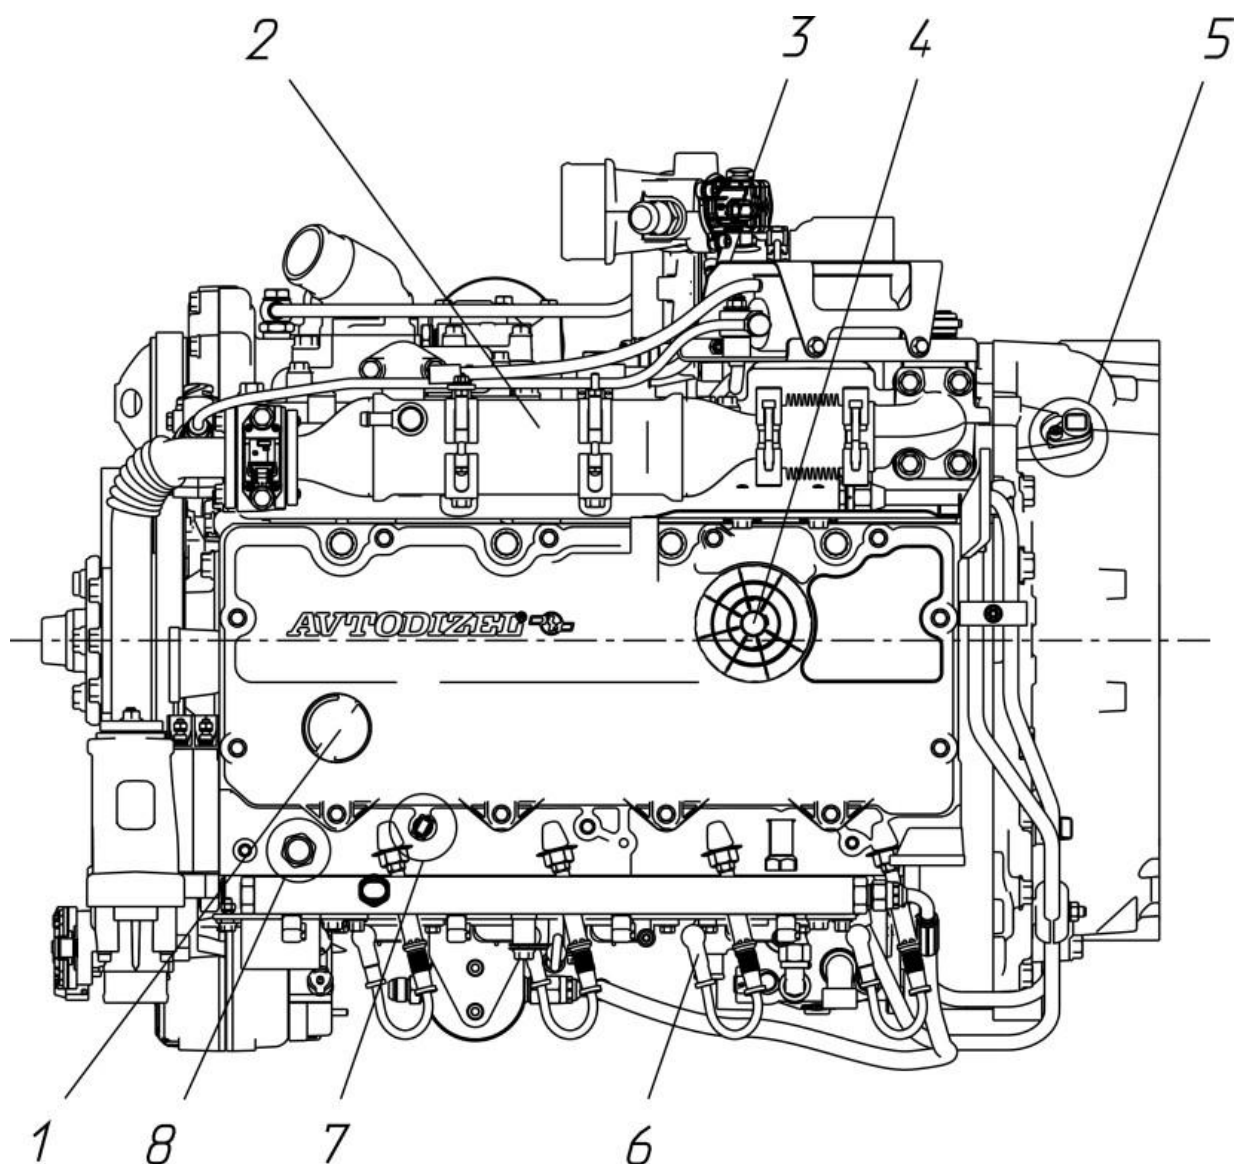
Расположение агрегатов и узлов двигателя ЯМЗ-53414 (вид сверху):
